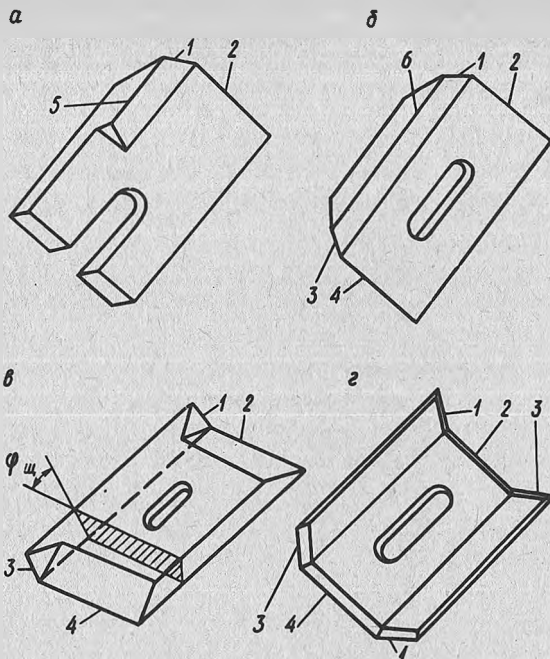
Режущие ножи: 1 - левая короткая режущая кромка; 2, 4 - длинная режущая кромка; 3 - правая короткая режущая кромка; 5 - выступ ограниченной длины; 6 - выступ на всю длину ножа.
